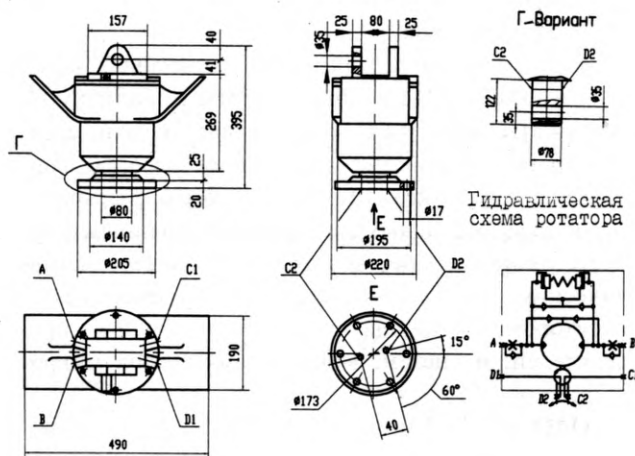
Ротор РУ-80 КЕТБ.063811.001 (габаритные и присоединительные размеры)
